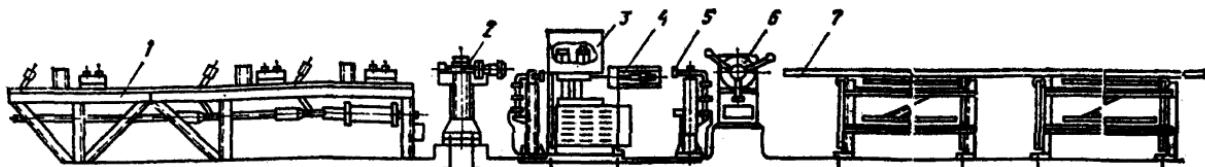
Установка СМЖ-524 для заготовки мерных стержней и высадки анкерных головок
